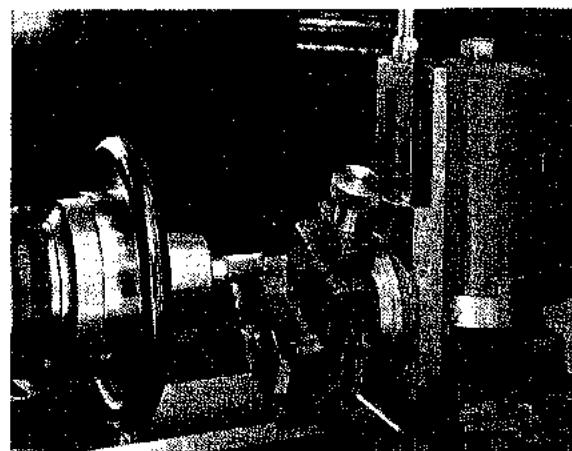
Aparato para fresar en el torno fijado a la ranura en T del soporte orientable (Cincinnati Lathe & Tool Co.)
